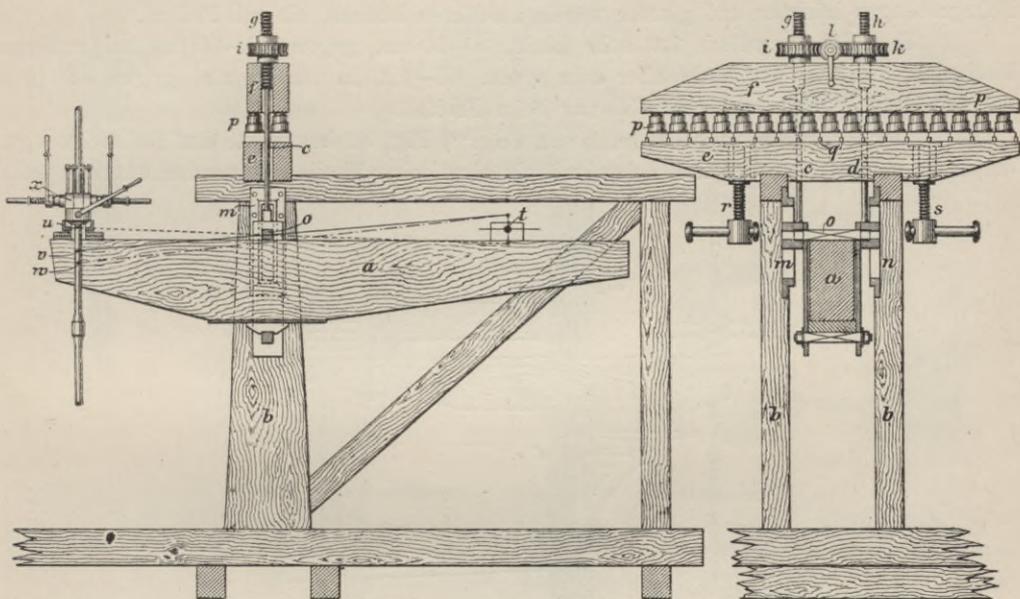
Elastischer Bohrschwengel von Raky. M. 1: 60. 1897.
